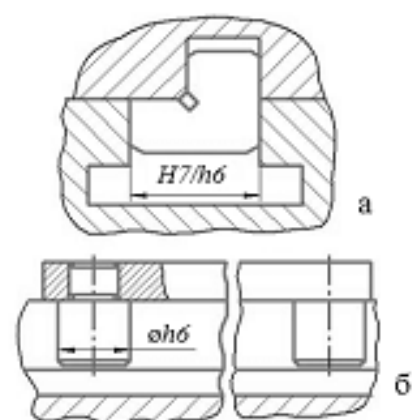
Орієнтуючі елементи фрезерних пристроїв
